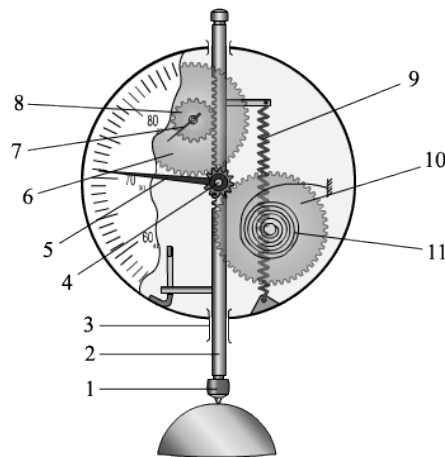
Пристрій індикатора годинникового типу: 1 – наконечник; 2 – вимірювальний стрижень – рейка; 3 – гільза; 4 – трибка; 5 – стрілка; 6 – передавальне зубчасте колесо; 7 – стрілка; 8 – зубчасте рейкове колесо; 9 – пружина; 10 – зубчасте колесо; 11 – пружинний волосок
